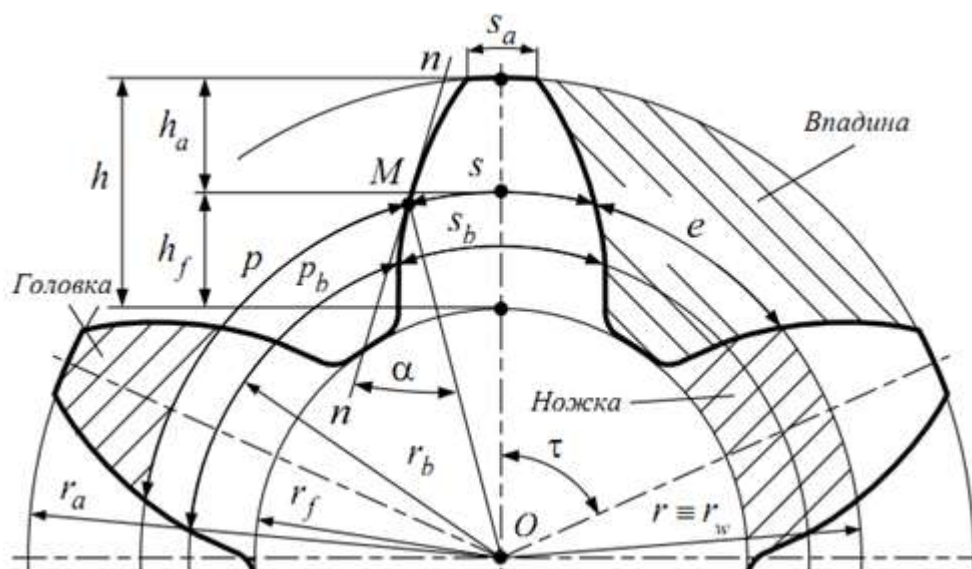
Основные параметры цилиндрического нормального колеса
